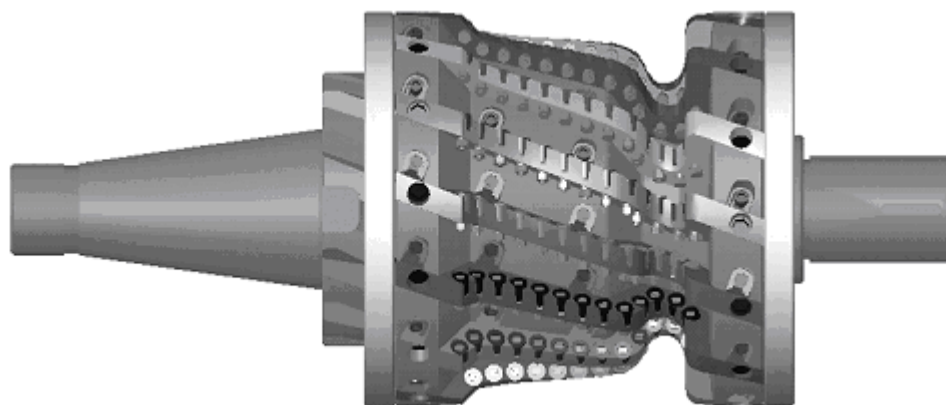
CAD модель фасонной фрезы к станкам КЖ-20
